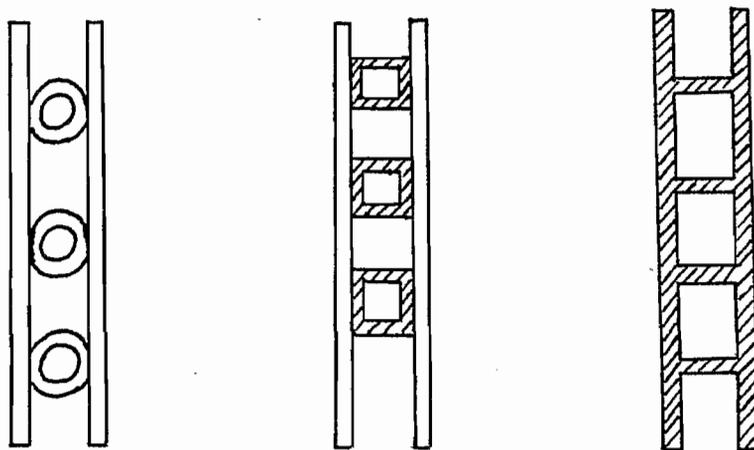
Forma de las placas de los congeladores de placas de contacto.
